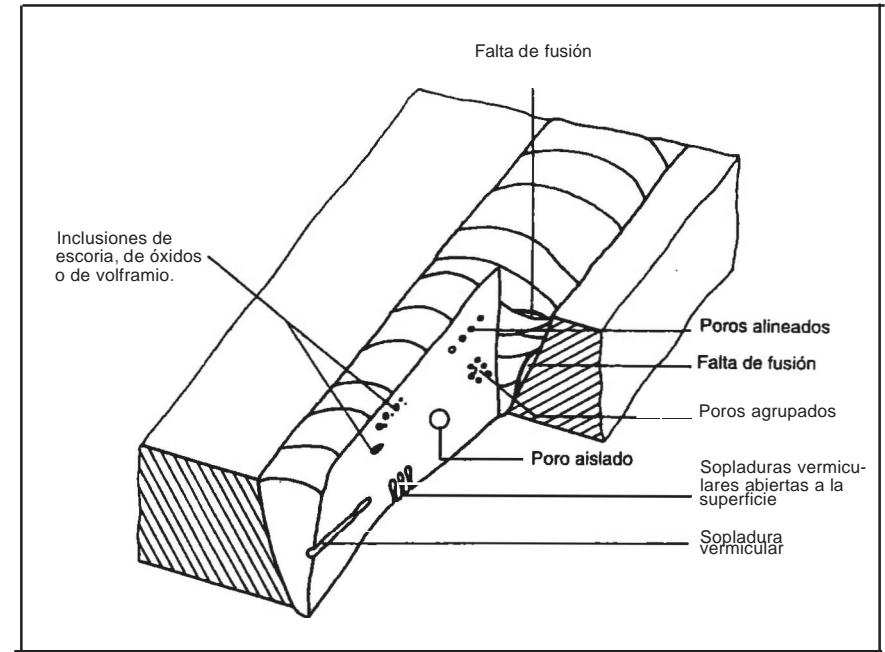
DEFECTOS INTERNOS EN UNA SOLDADURA
